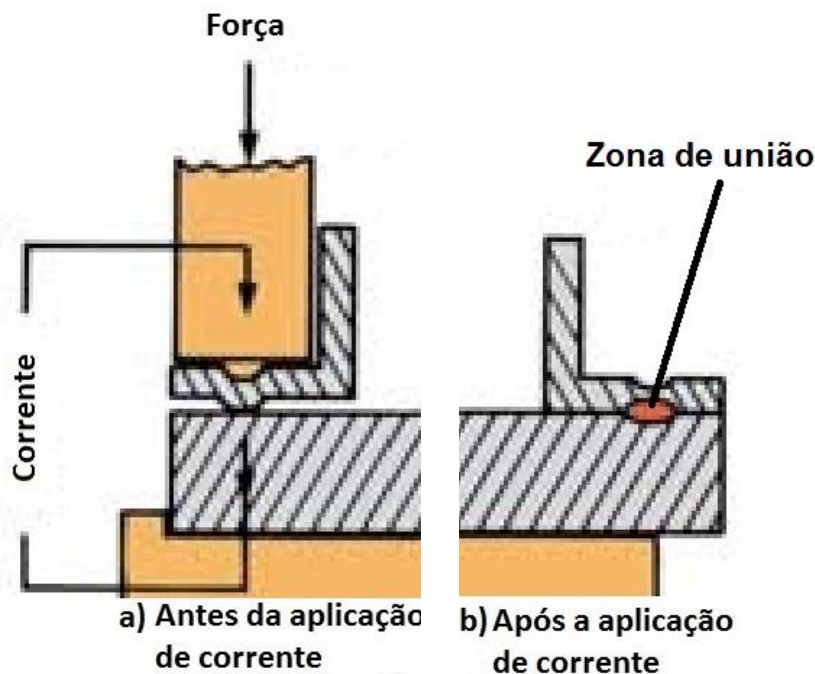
Esquema do processo de soldadura por protuberâncias, (a) antes e (b) após a aplicação de corrente elétrica [28].
